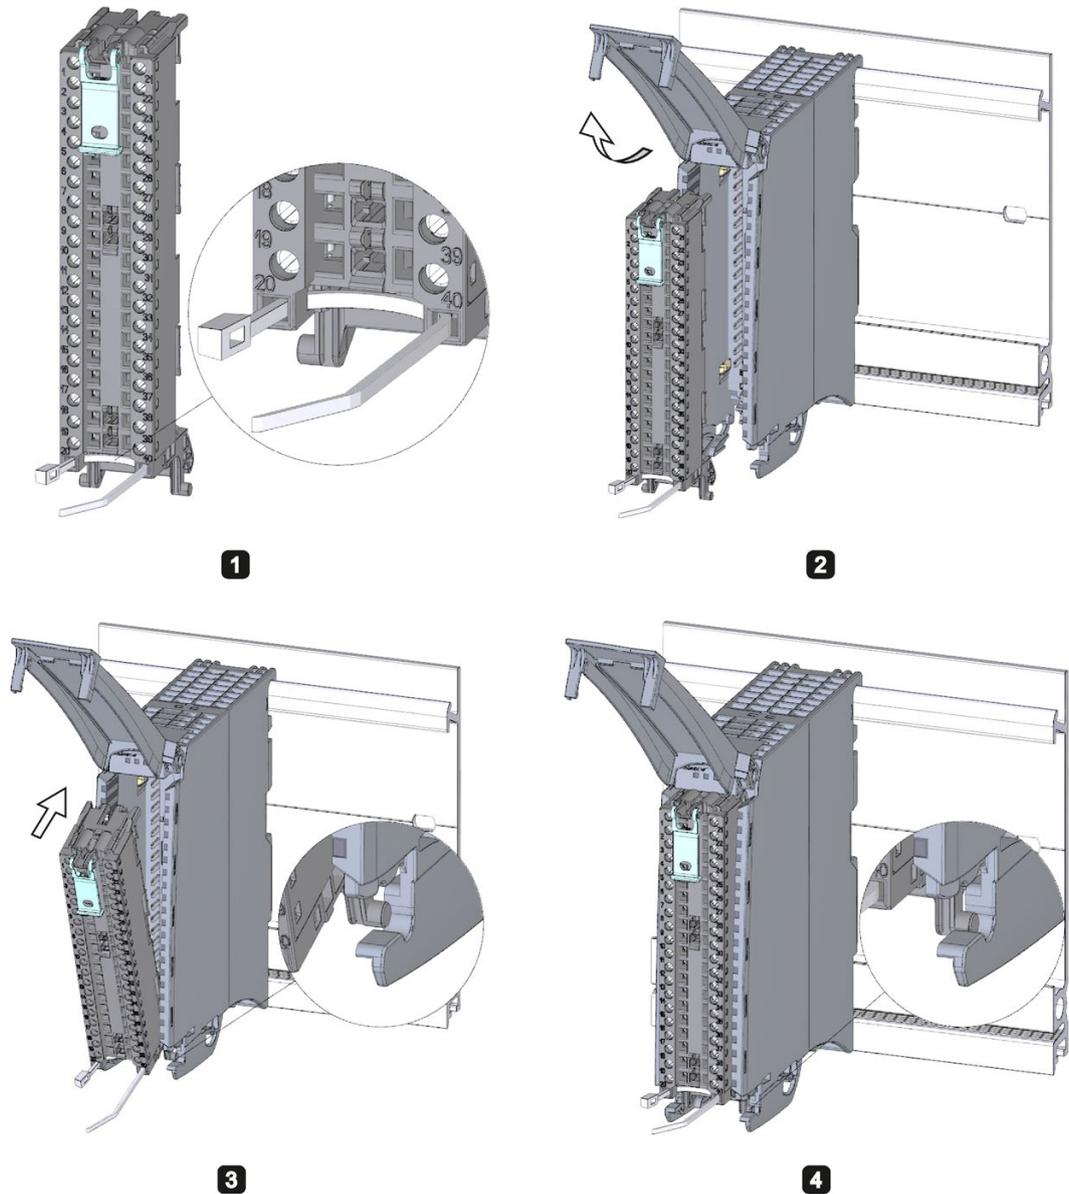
Cableado del conector frontal para módulos de periferia sin elemento de contacto de pantalla
